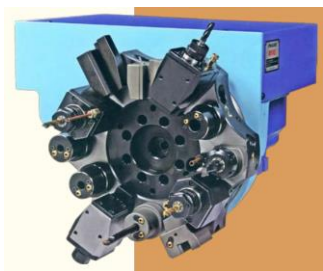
Револьверна головка із торцевим (осьовим) кріпленням інструменту
